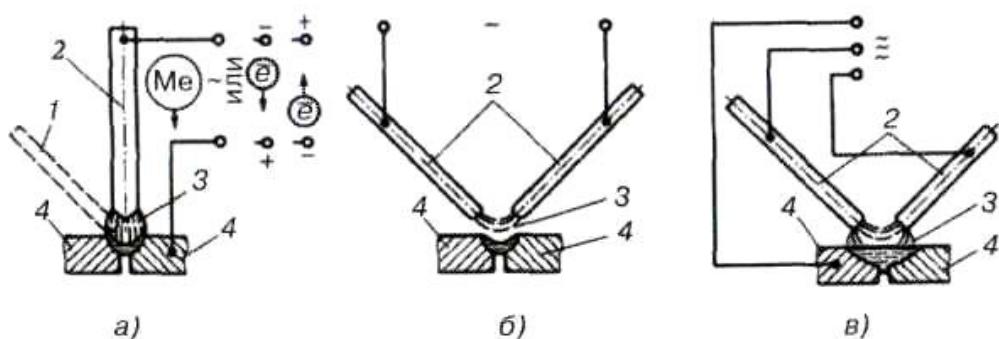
Схемы дуговой сварки: а - ; б - ; в - ;
